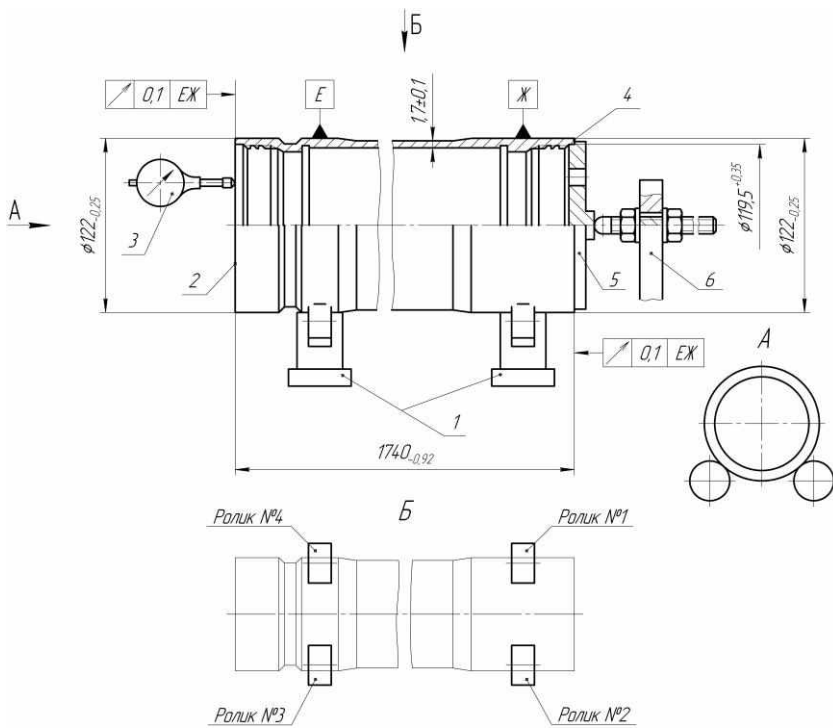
Схема контроля биений торцов базовой детали: 1 – роликовые призмы; 2 – торец № 1; 3 – индикатор часового типа; 4 – торец № 2; 5 – заглушка; 6 – упор
